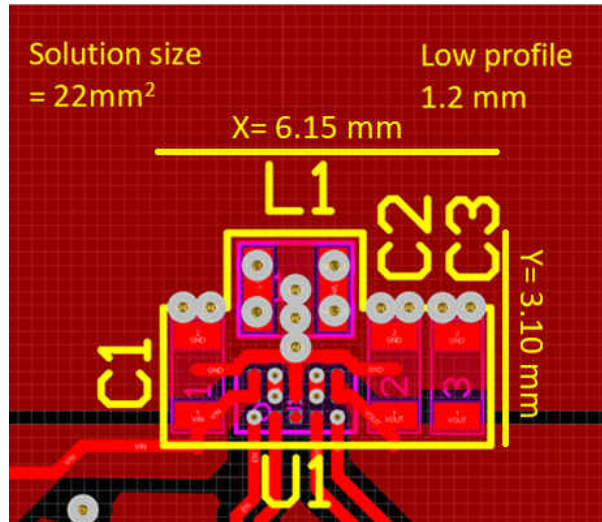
TPS63810 的 PCB 布局，解决方案尺寸仅为 22mm^2
